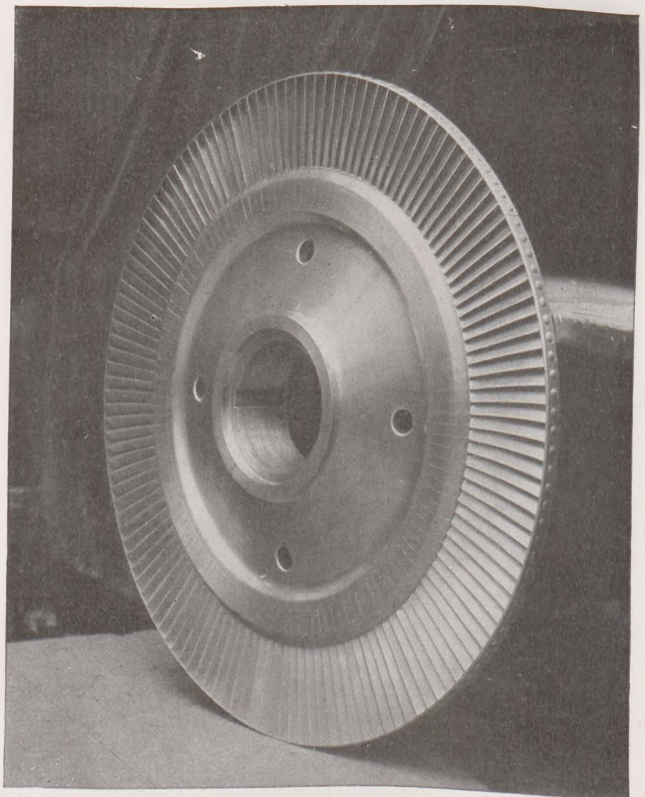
Laufrad mit Monel-Metall-Schaufeln und Deckbänder für ein Turbospeisepumpen-Aggregat.
